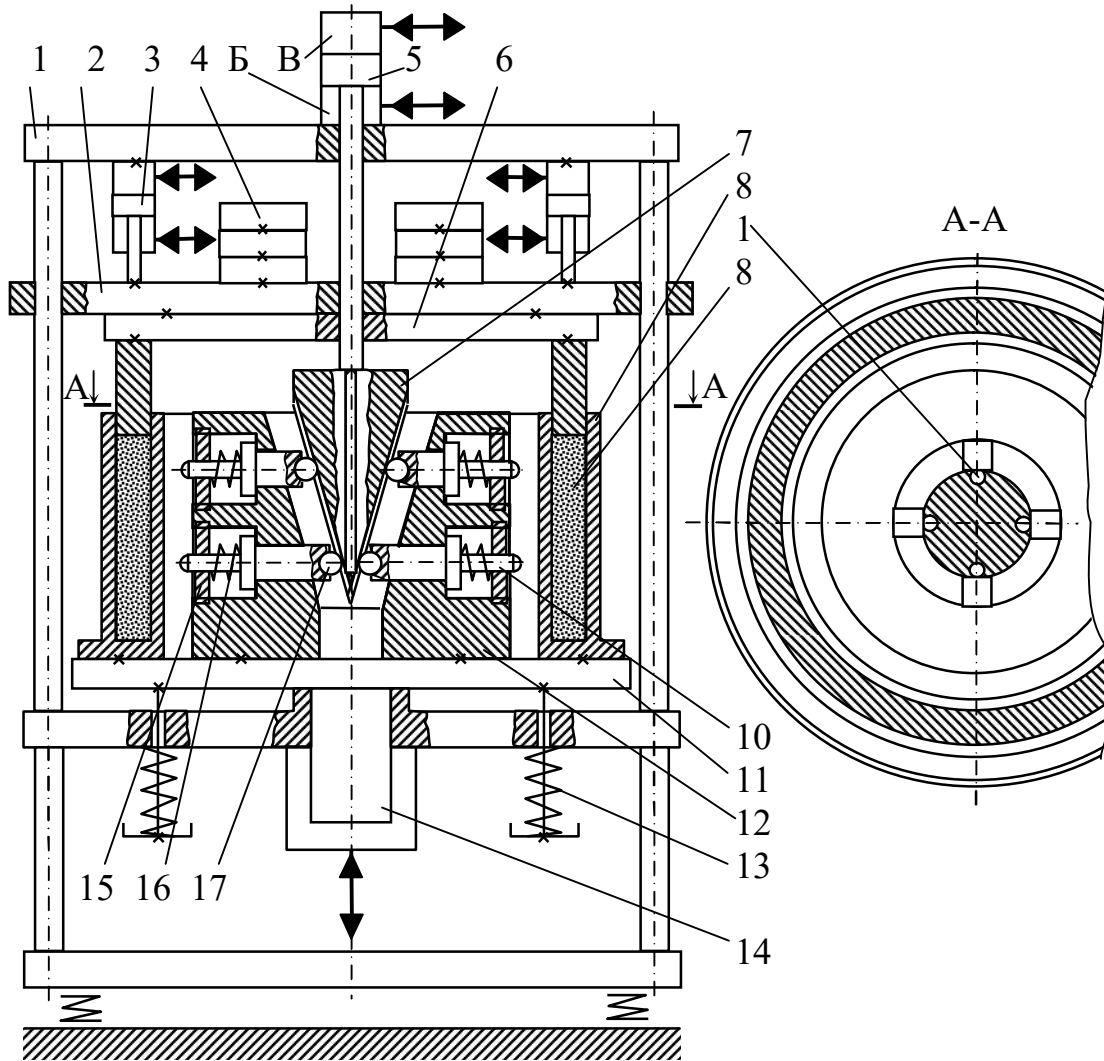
Конструктивна схема вібропреса для БКВН великогабаритних кільцеподібних заготовок на базі ІВПМ
